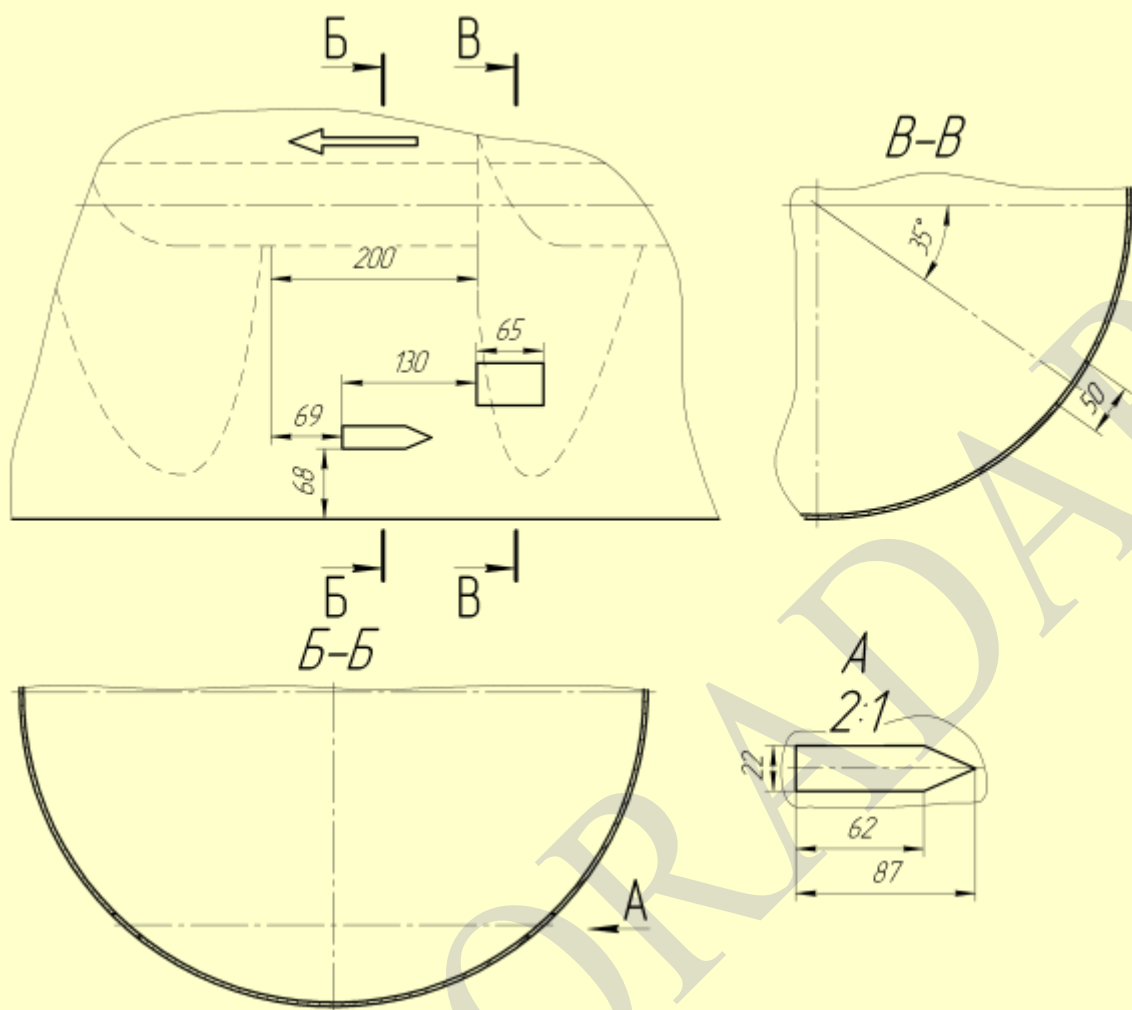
Подготовка шнекового транспортёра. Стрелкой указано направление движения
